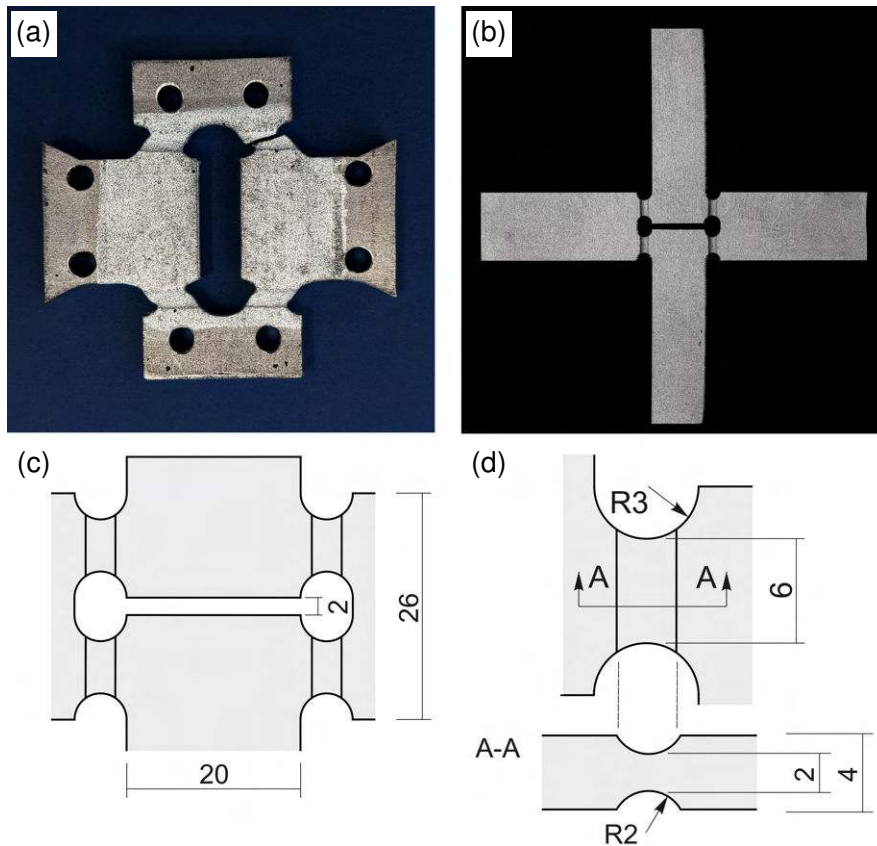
Diferentes geometrías a evaluar y dimensiones: (a) probeta corta (rota) - 5 cm, (b) probeta larga - 15 cm, (c) dimensiones generales, (d) detalle entalla. Dimensiones en [mm].
